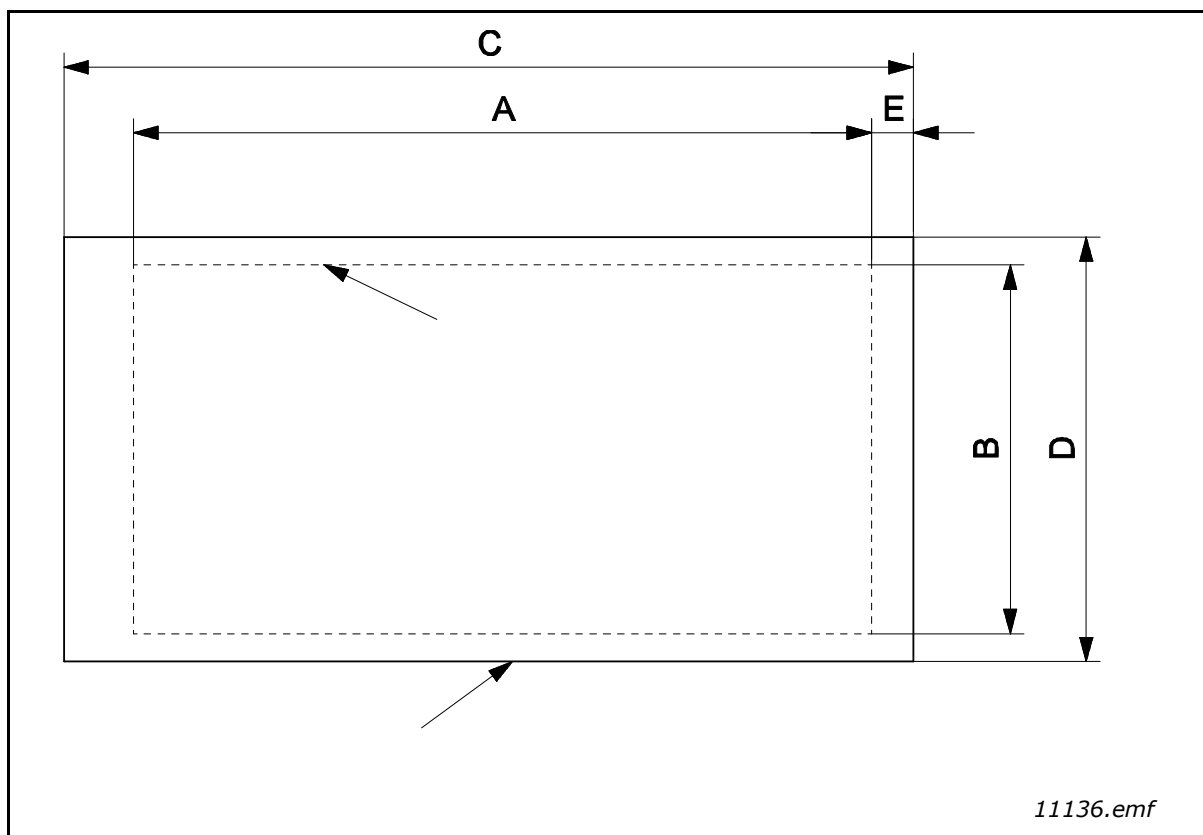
Dimensiuni de decupare pentru montare cu flanșă la gabaritele MR4 până la MR9
